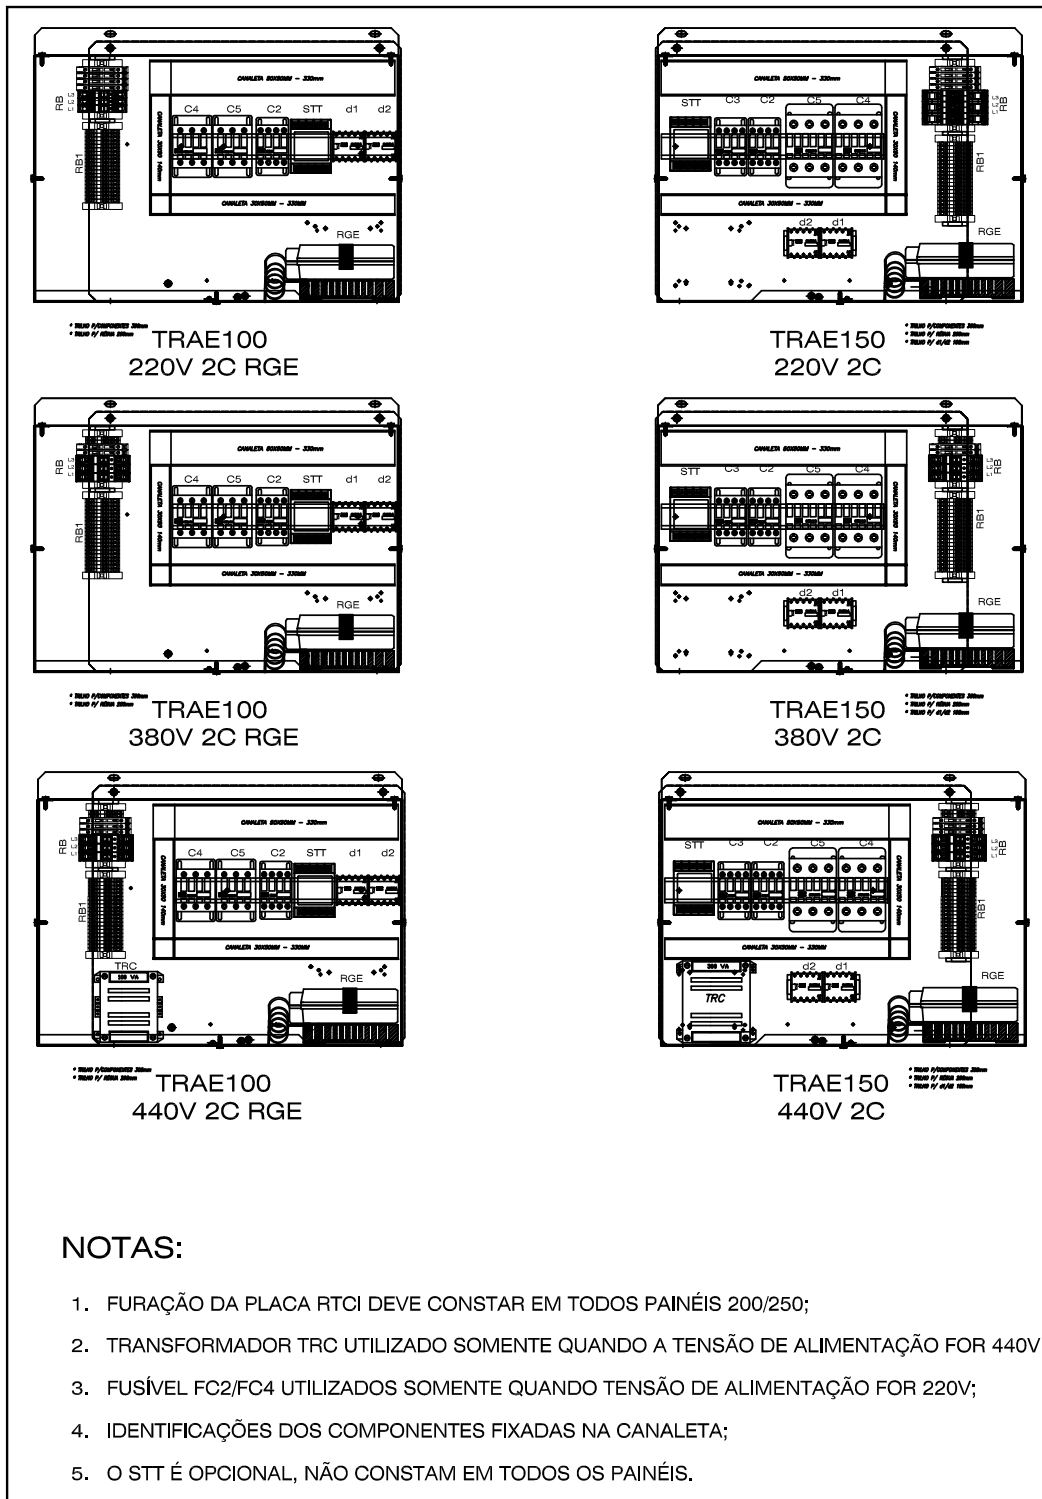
Lay Out de Tableros Eléctricos - TRAE (RTRM)
